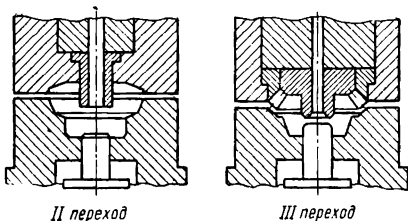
Схема штамповки шестерни с оформлением зубьев в окончательном переходе
